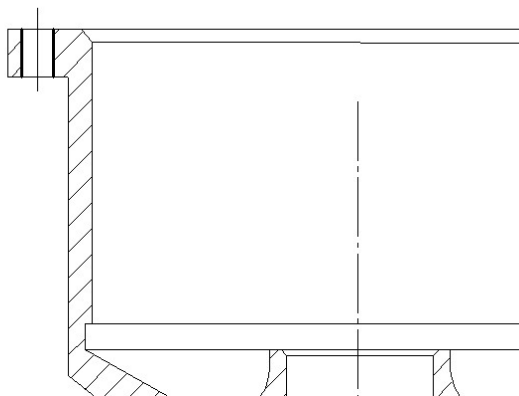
Схема базування заготовки корпус гідроциліндра
